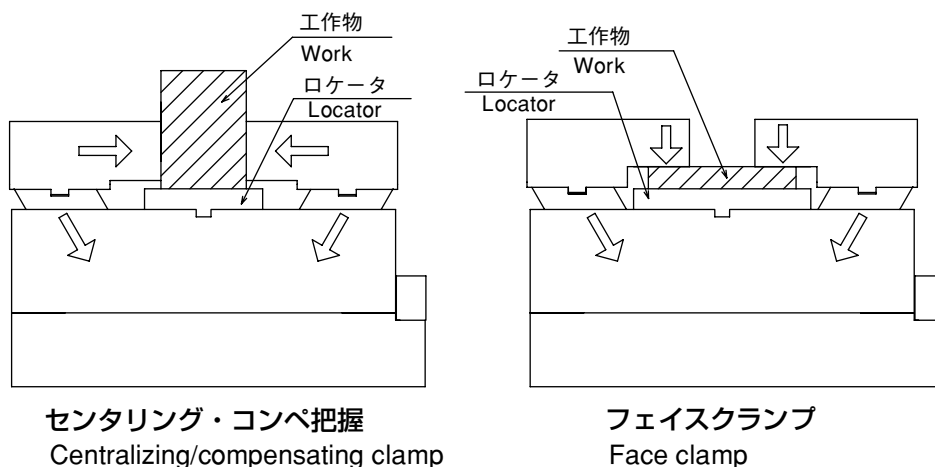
治具モジュール把握方法 Clamping Method of Jig Module
